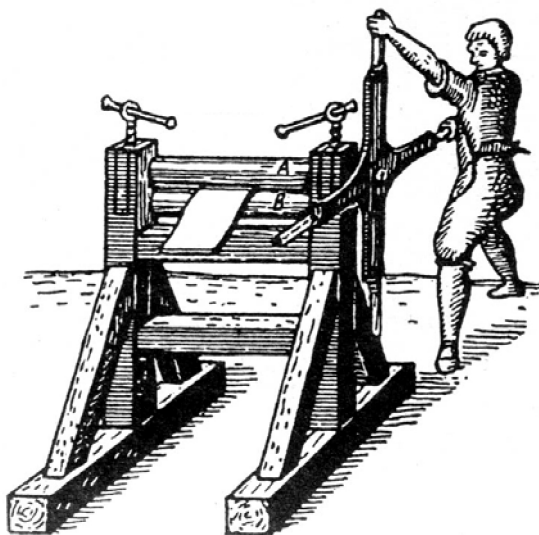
Прокатный стан дуо с цилиндрическими валками
